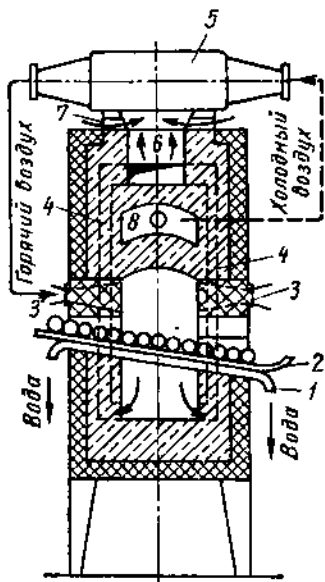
Схема устройства перекаточной печи с рекуператором для скоростного газового нагрева
